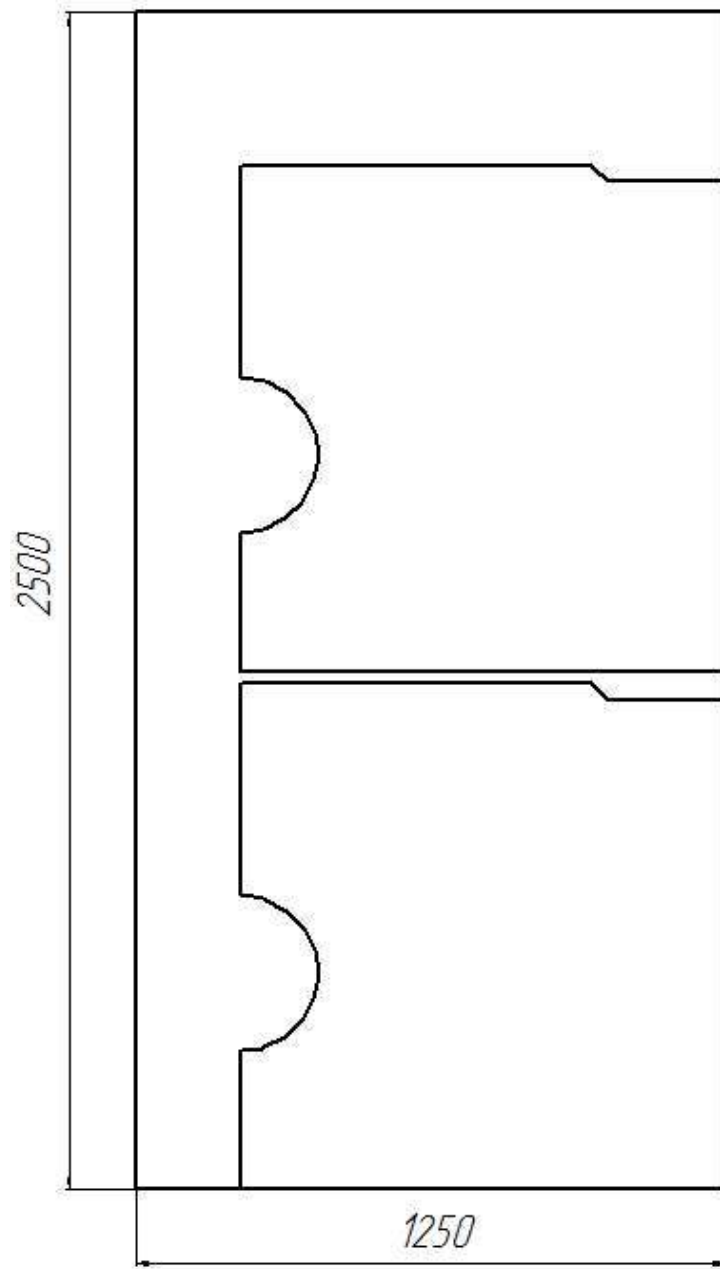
Схема різання листа 2500x1250x2 мм, на 2 заготовки
